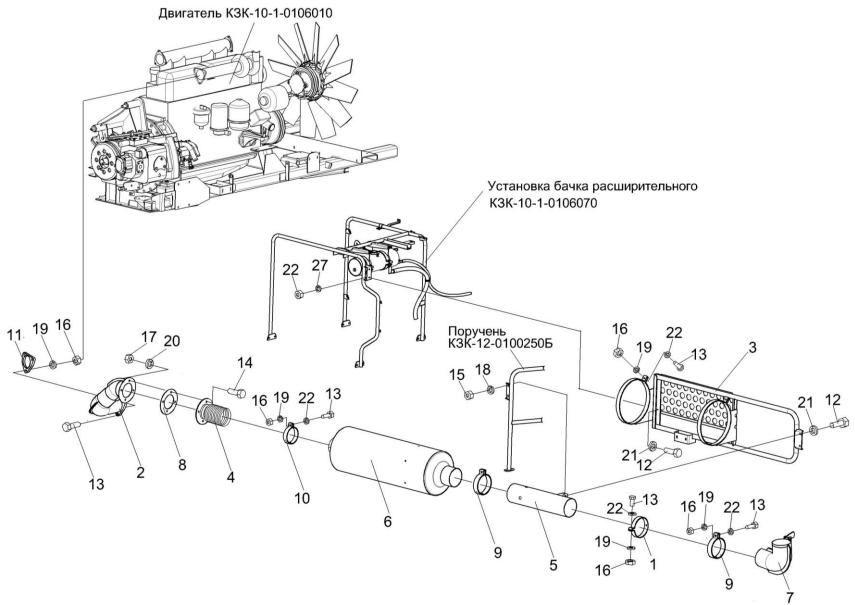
Установка глушителя КЗК-10-1-0106060
